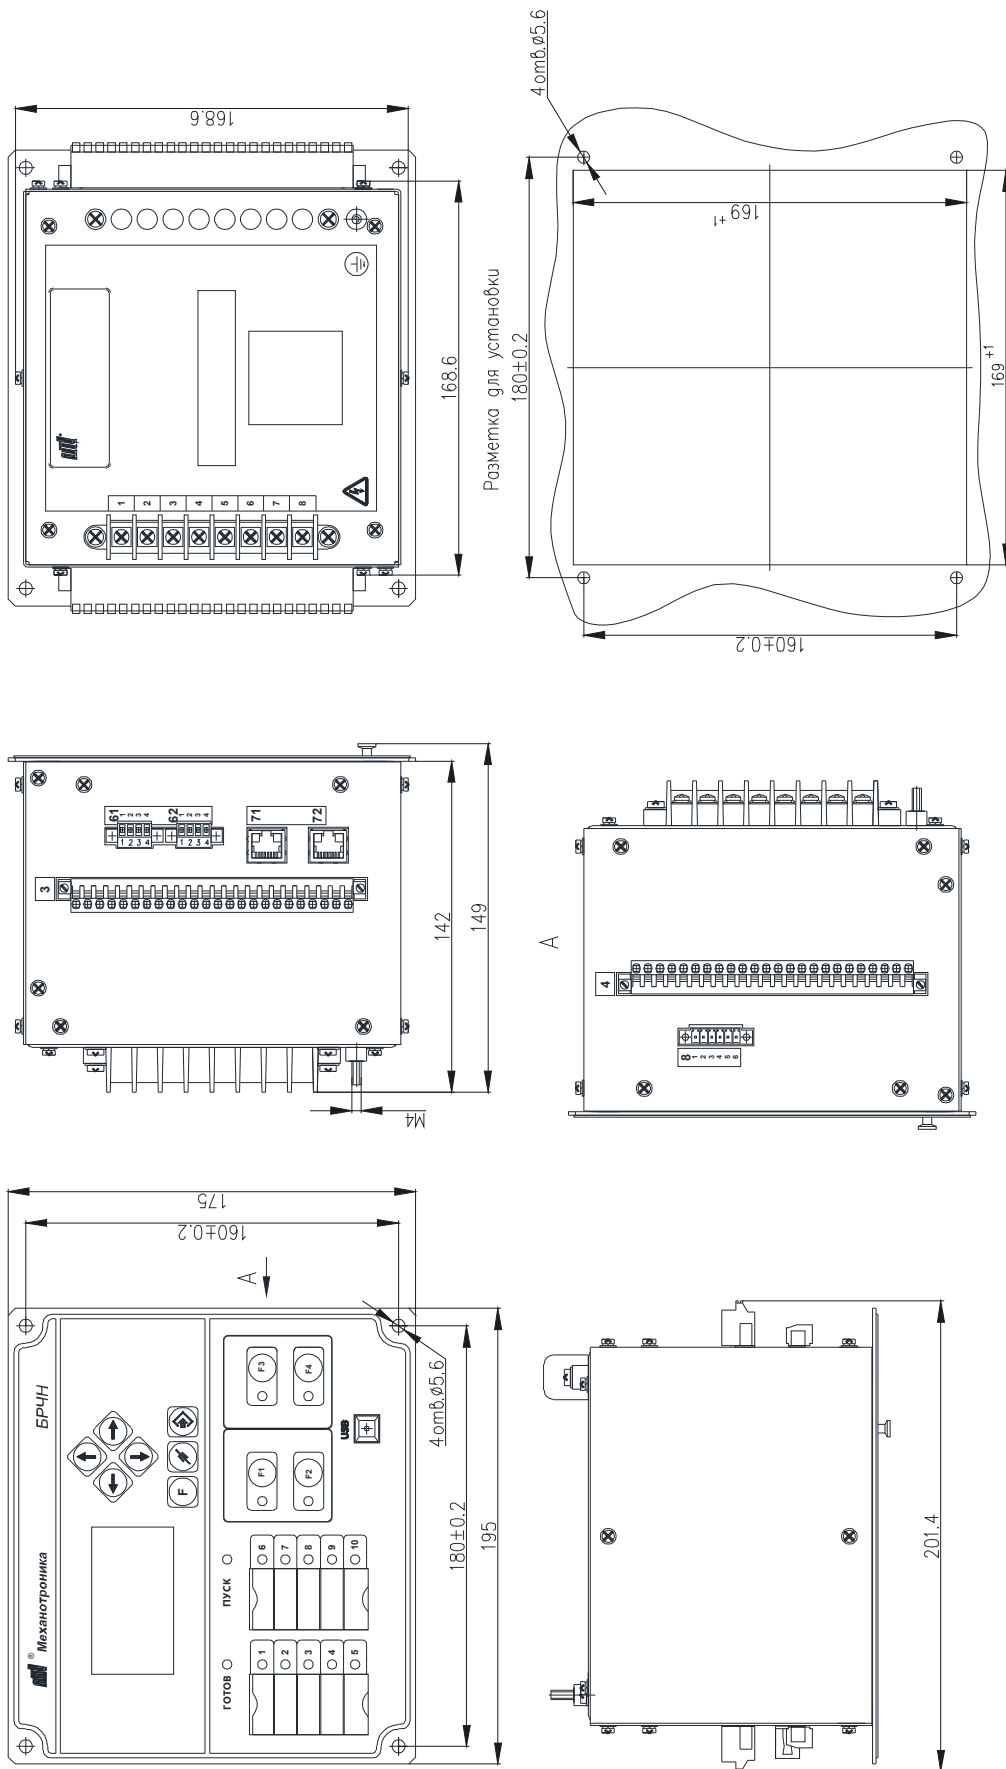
Габаритные и установочные размеры, внешний вид блока
